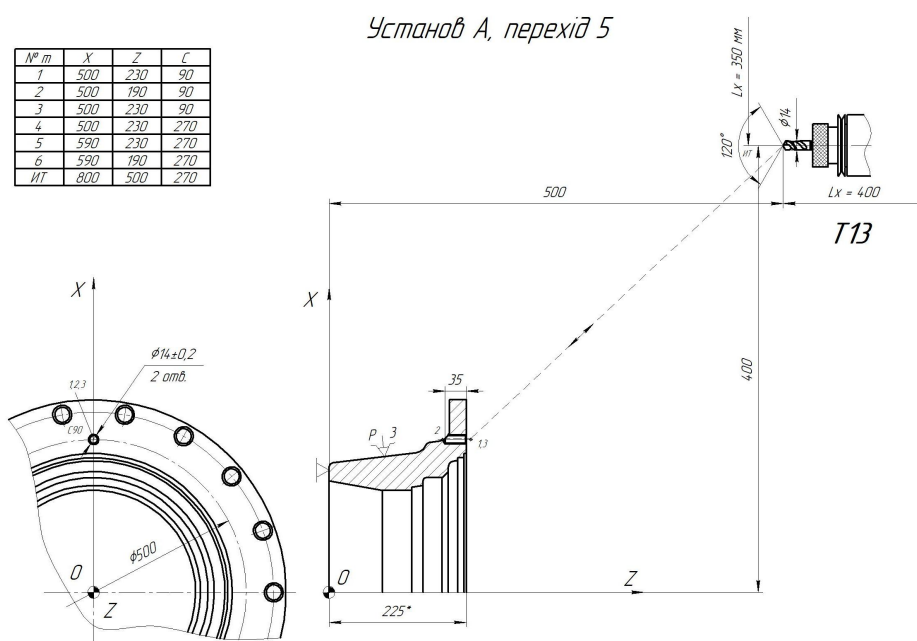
Установка А, перехід 5: схема обробки деталі та координатне розташування інструмента
